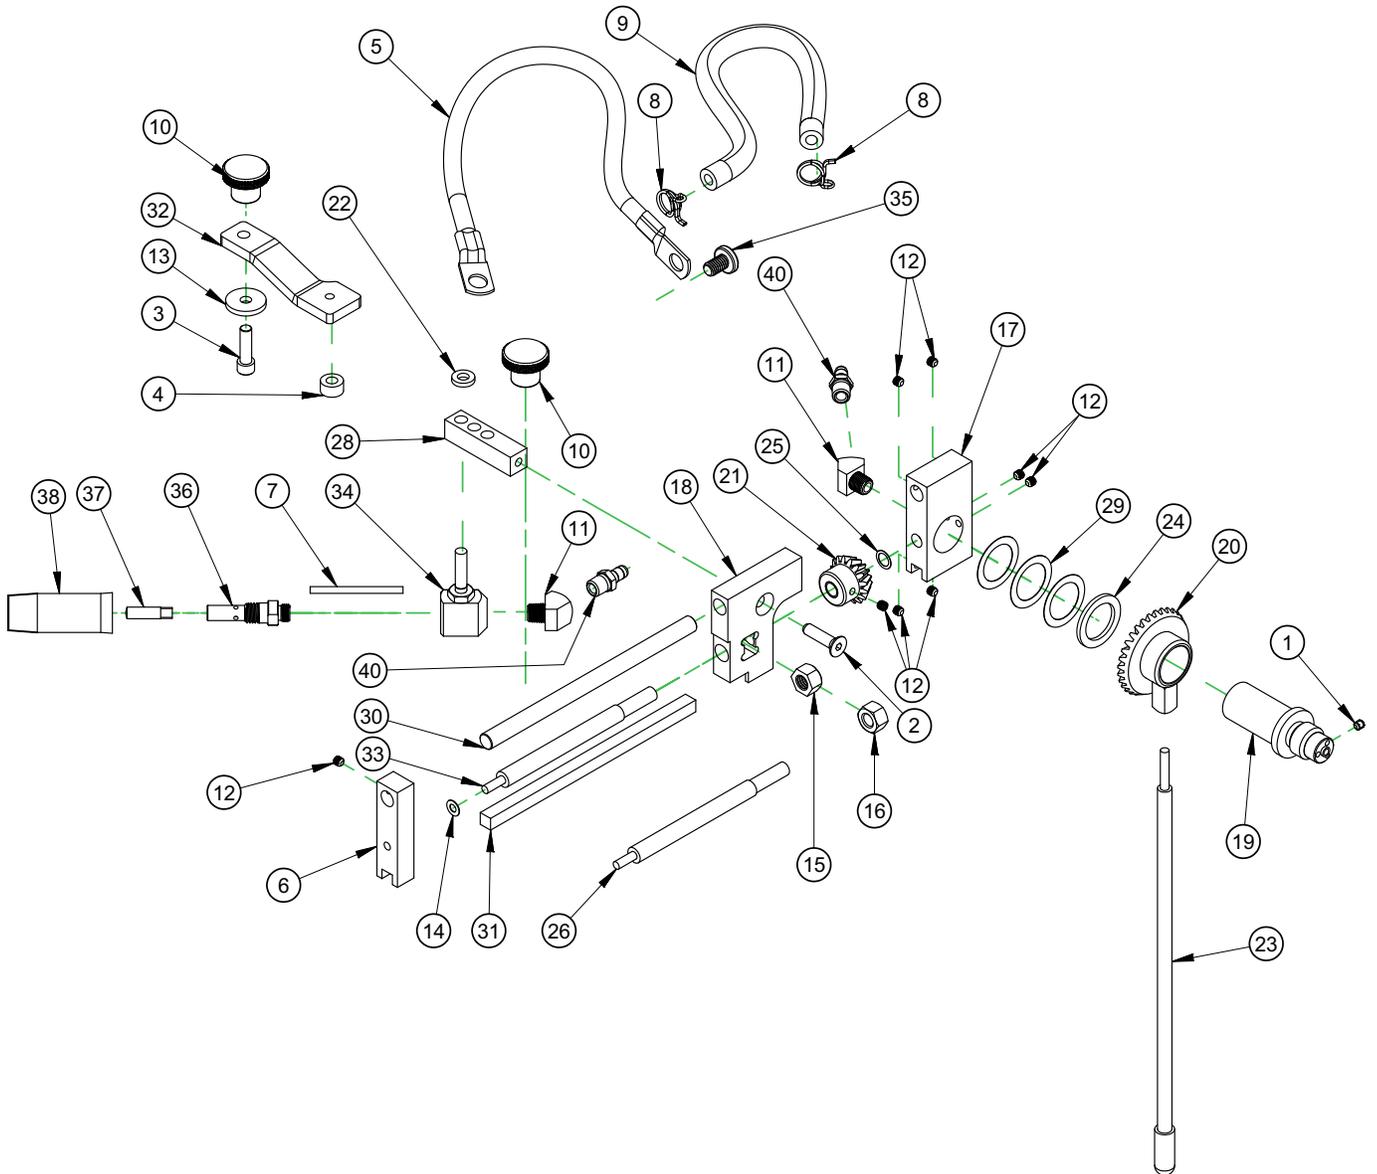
ENSEMBLE TORCHE DE SURFACE COMPACT 152 MM (RÉF. 48013)
